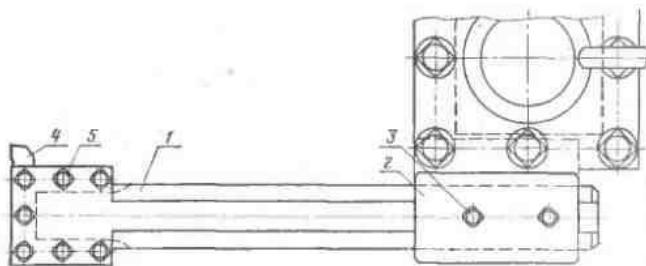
Резцовая оправка для обработки деталей над выемкой в станине
